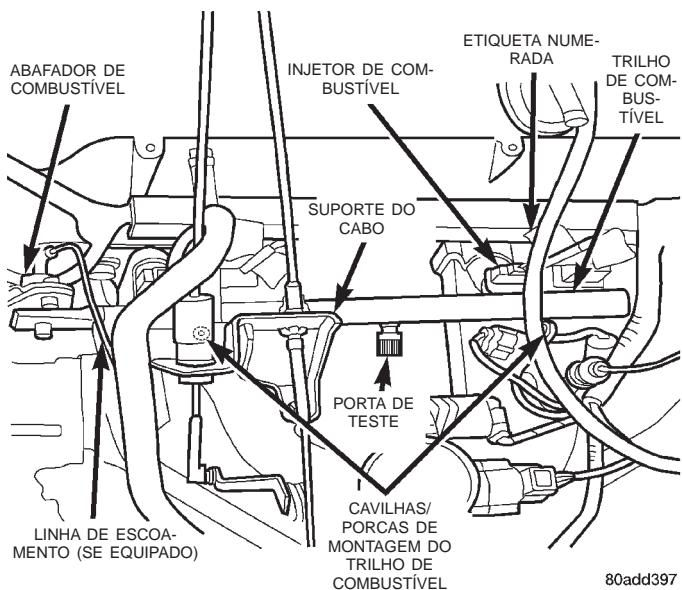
Montagem do Trilho de Combustível— Motor 2.5L
